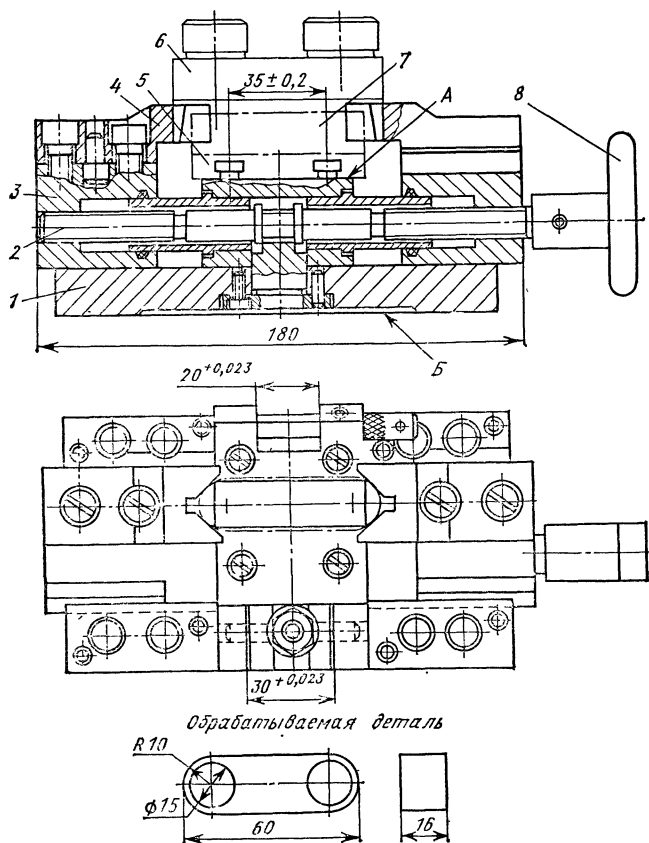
Переналаживаемый кондуктор для сверления отверстий в деталях типа планок и шпонок
